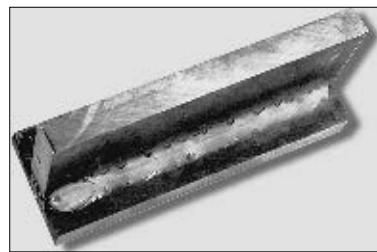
Внешний вид углового шва, выполненного в смеси Ar+20% CO₂ проволокой диаметром 1,2 мм (сварочный ток 260 А, напряжение 28 В)
